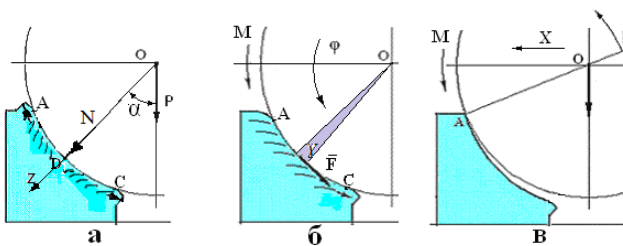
Складові переміщення валка по поверхні заготовки
